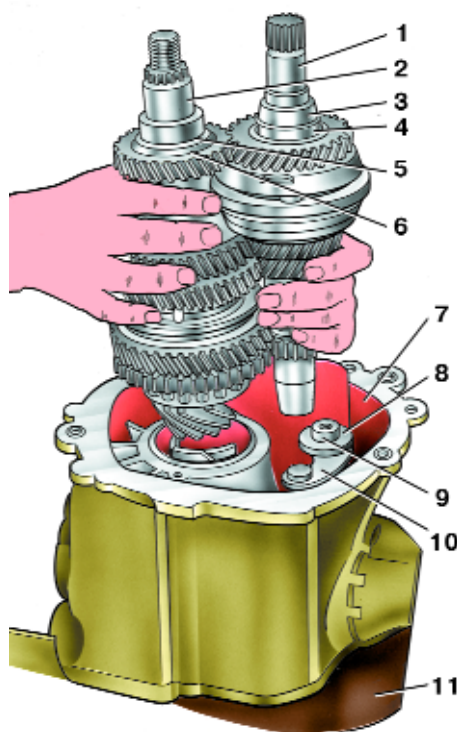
Извлечение из картера главной передачи соединенных вместе первичного и вторичного валов: 1 – первичный вал в сборе с шестернями; 2 – ведущая шестерня главной передачи (вторичный вал) в сборе с шестернями; 3 – переднее кольцо подшипника; 4 – упорная шайба четвертой передачи; 5 – переднее кольцо подшипника; 6 – регулировочная шайба; 7 – картер главной передачи; 8 – промежуточная шестерня заднего хода (зубчатый венцом обращена вниз к стенке картера); 9 – ось заднего хода; 10 – вилка включения заднего хода; 11 – деревянная подставка
